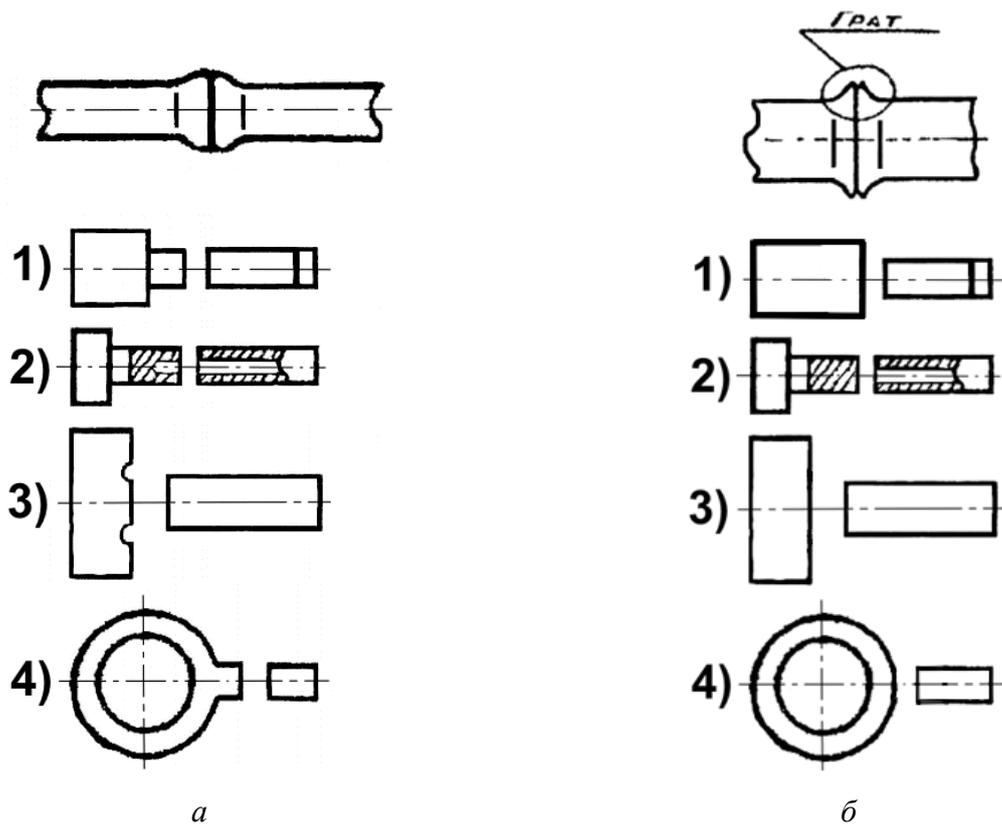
Виды сварных соединений при КСС (а) и КСО (б)
